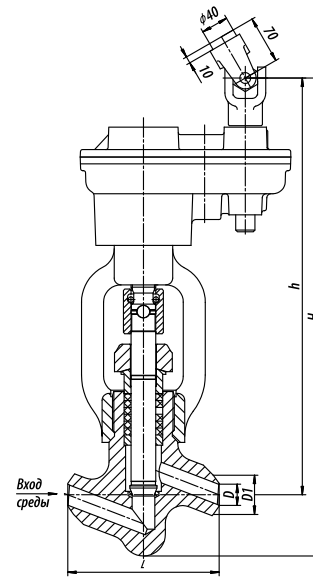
а. Клапан запорный DN32-65 с цилиндрическим редуктором
